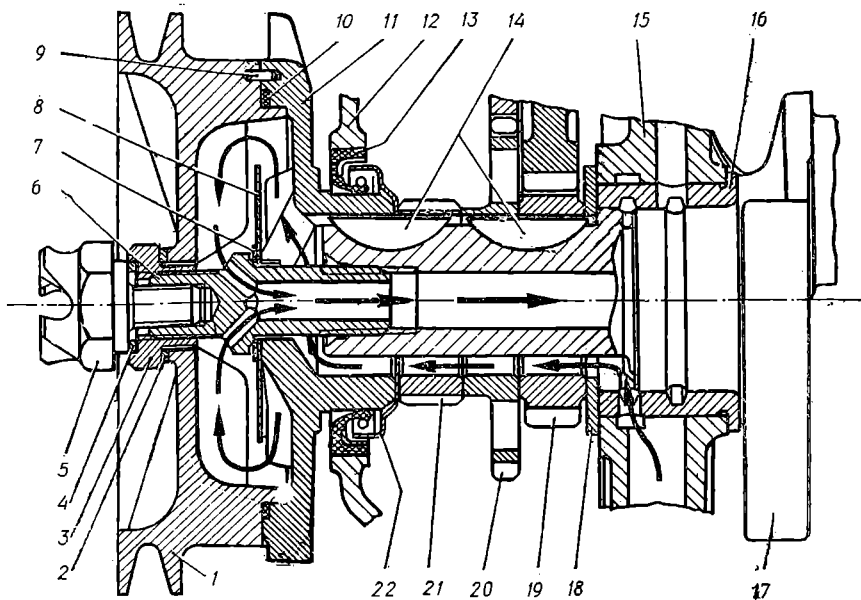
Центробежный маслоочиститель и передний коренной подшипник коленчатого вала:
